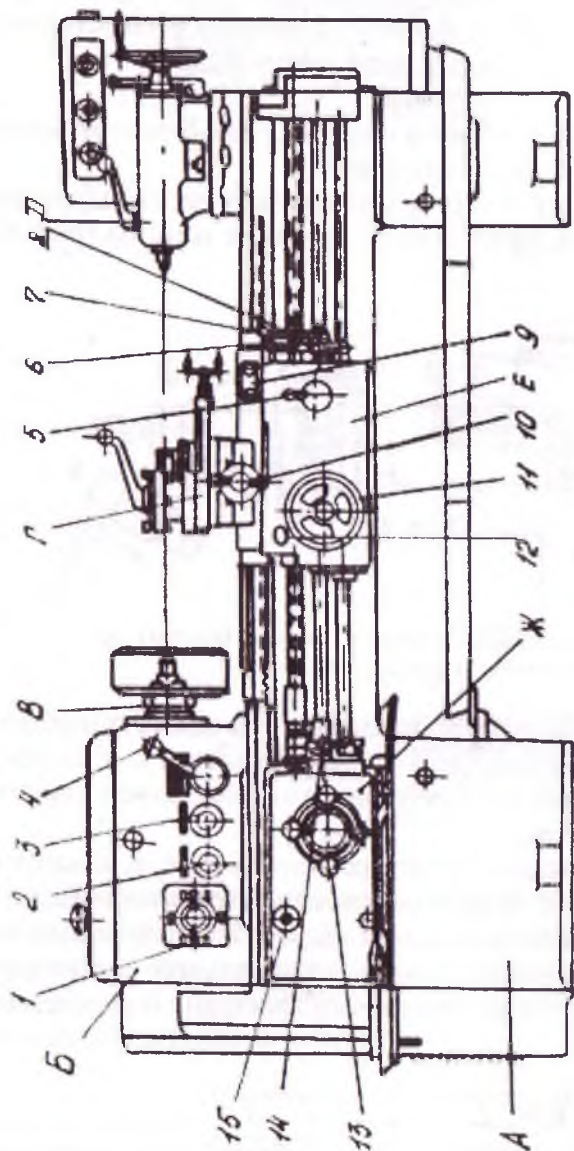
Общий вид основной части и органы управления станка 1К62: 1,4 - рукоятки переключения скоростей шпинделя; 2,3 - рукоятки для включения звена увеличения шага и вида резьбы (правая, левая); 5 - рукоятки для включения маховой гайки винтовой пары; 6,14 - рукоятки переключения фрикционной муфты и ленточного торможения для пуска, реверсирования и останковки шпинделя; 7 - кнопка включения ускоренного перемещения суппорта; 8 - рукоятка управления движениями суппорта; 9 - кнопки включения и выключения главного электродвигателя; 10,13 - рукоятки установления величины подачи и шага резьбы; 15 - рукоятки для включения на подачу, резьбу и архимедову спираль; 10 - рукоятка ручной поперечной подачи салазок суппорта, 11 - маховик ручной продольной подачи суппорта; 12 - кнопка для выключения реечной шестерни при нарезании резьбы.
